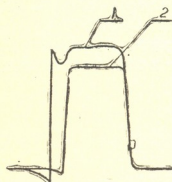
Профили и размеры оправок: 1 — старой калибровки, 2 — новой калибровки
